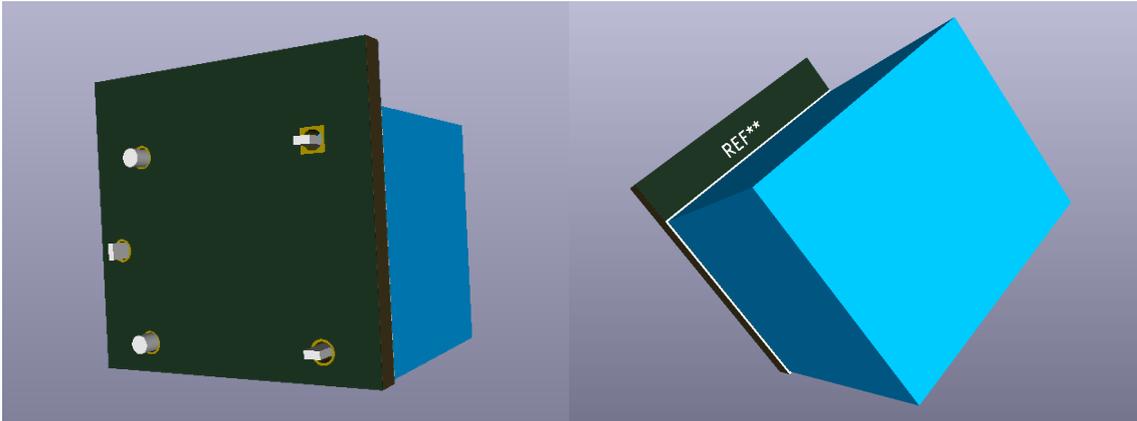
Visor 3D del relé SRD-5VDC-SL-C sobre su huella en la herramienta de diseño KiCad.
